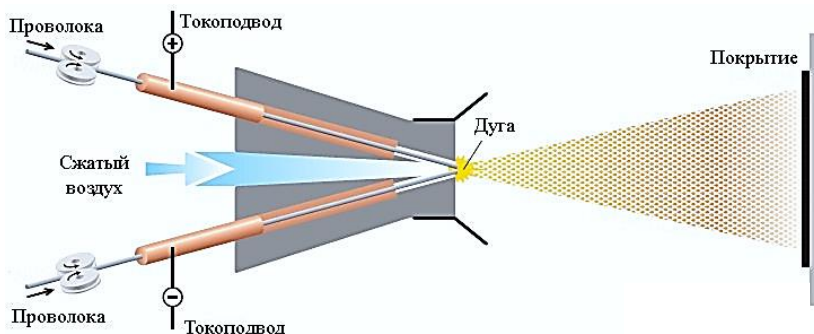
Схема дуговой металлизационной установки [8]
